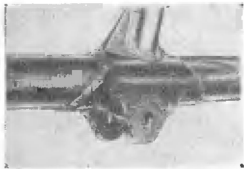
Узел 6 — крепление заднего дополнительного лонжерона центроплана.
